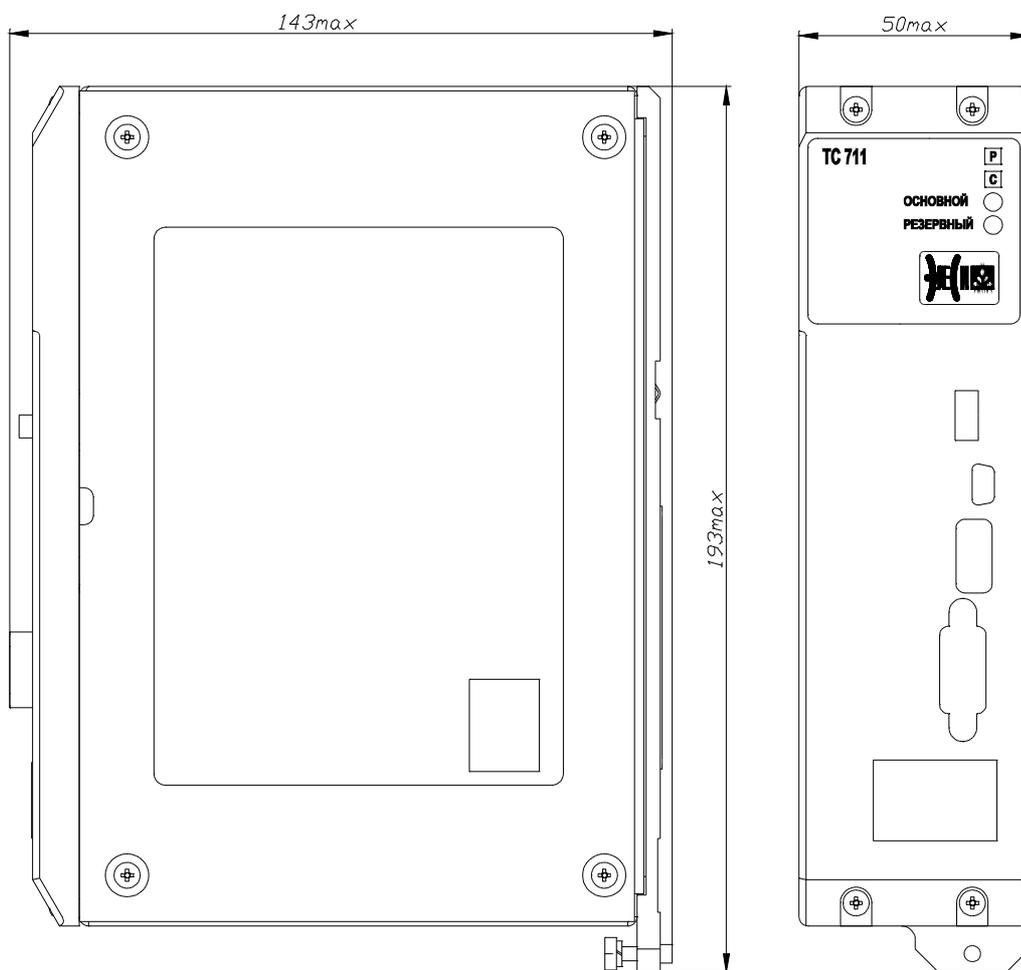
Модуль ТС 711. Габаритный чертеж
